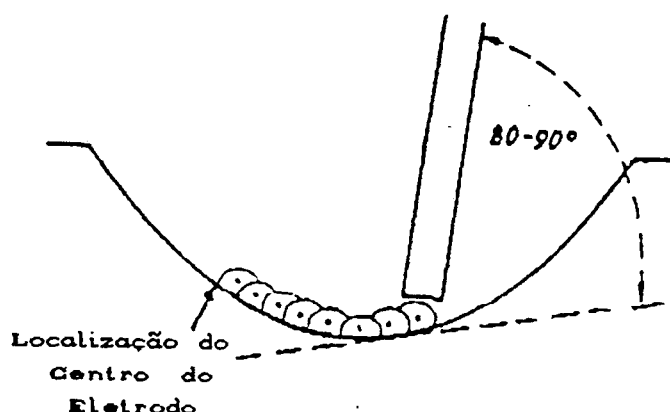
Direcionamento do Eletrodo na Soldagem
